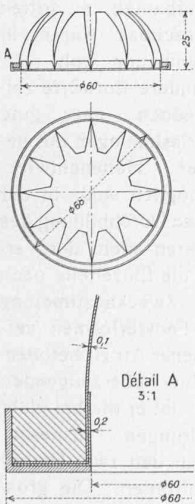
Clapet, 1 : 3. Coupe, plan et détail.
